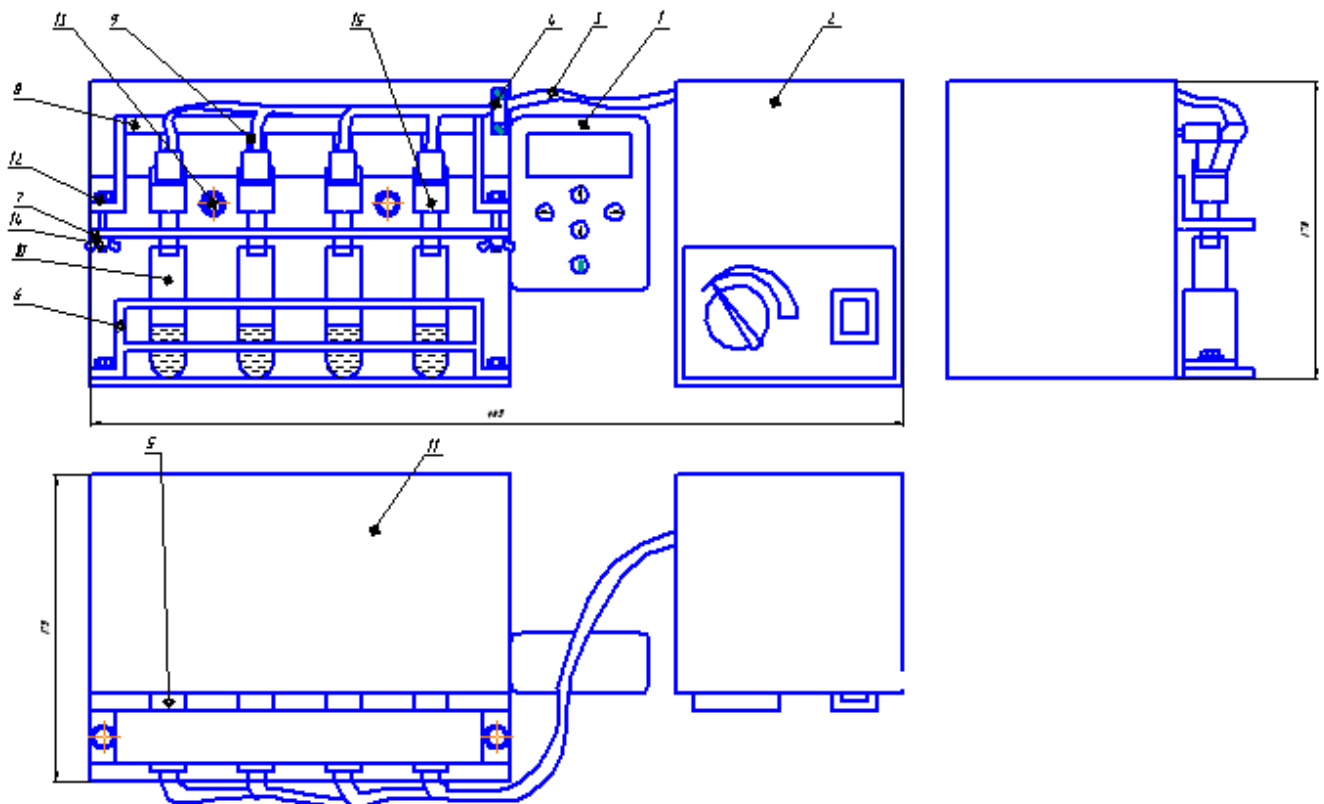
Стенд для перевірки і промивки форсунок
